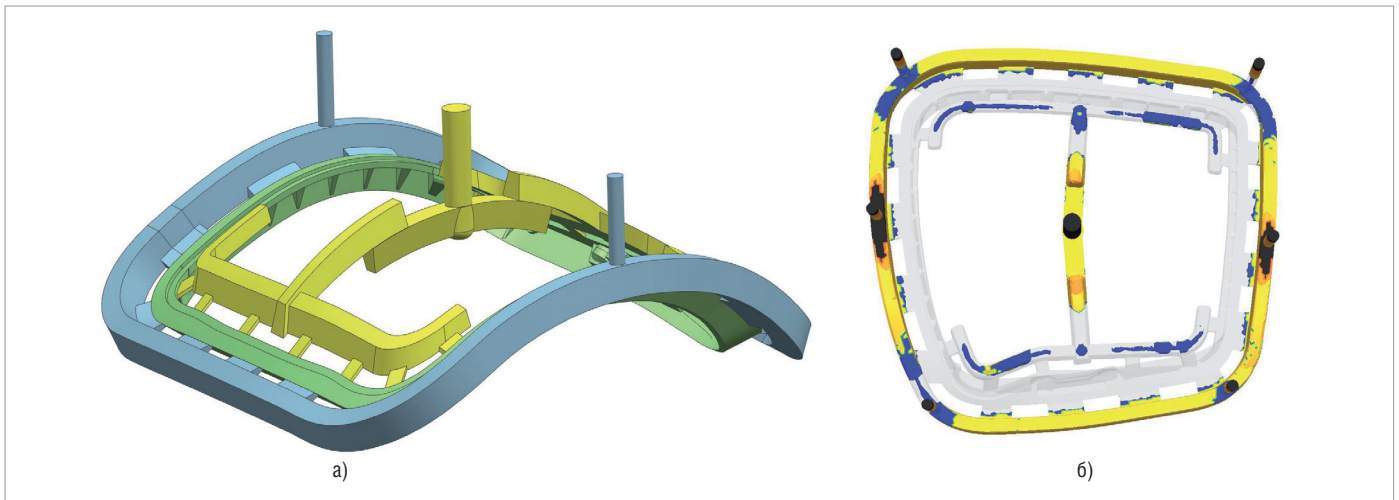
Новая конструкция ЛПС для отливки типа "Рама": а) 3D-модель литейного блока; б) результат прогноза пористости
